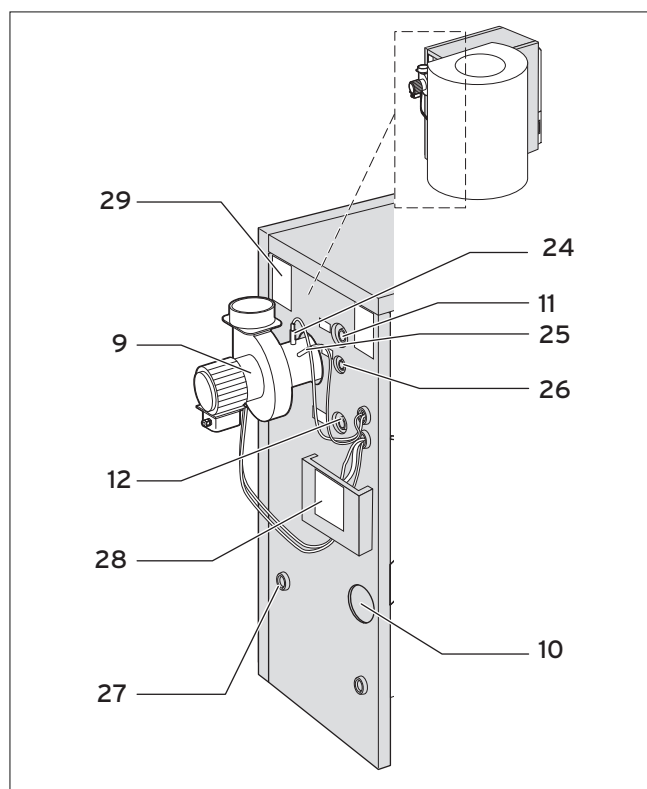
Rückansicht des Pellet-Heizkessels mit Saugaustragung
